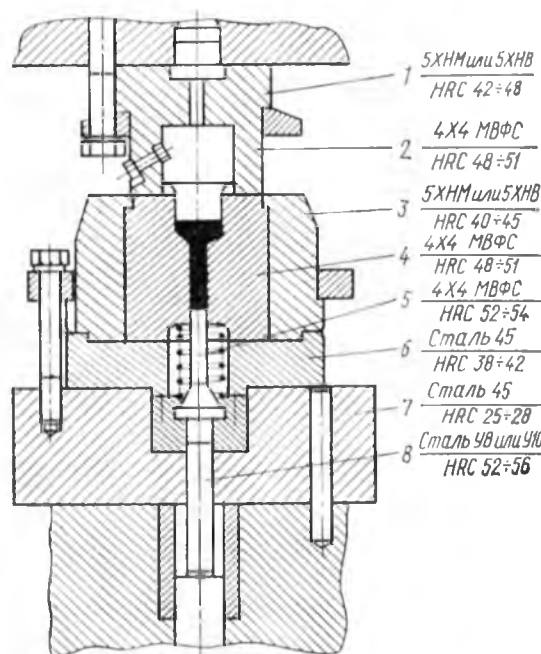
Марки стали и нормы твердости основных деталей штампа для выдавливания поковок пазовой фрезы из стали Р18 на высокоскоростном молоте:
